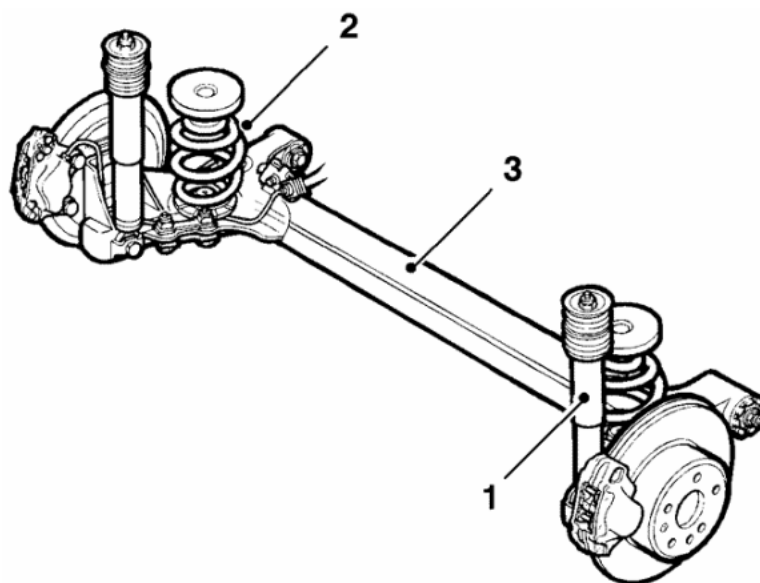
U stabilizátor spojen s pružící jednotkou pomocí táhla
